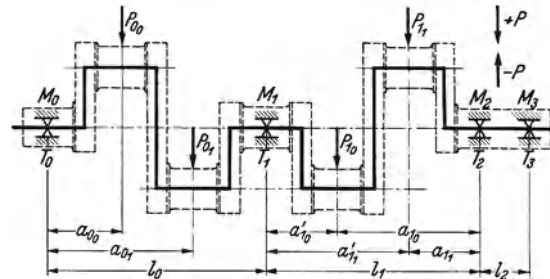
Ermittlung der Lagermomente und Lagerdrücke an einer 4-Zylinder-Welle mit 3 Lagern.
